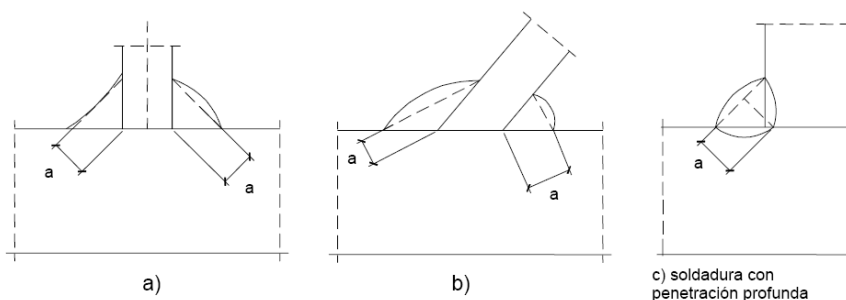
Soldadura en ángulo. Espesor de garganta
